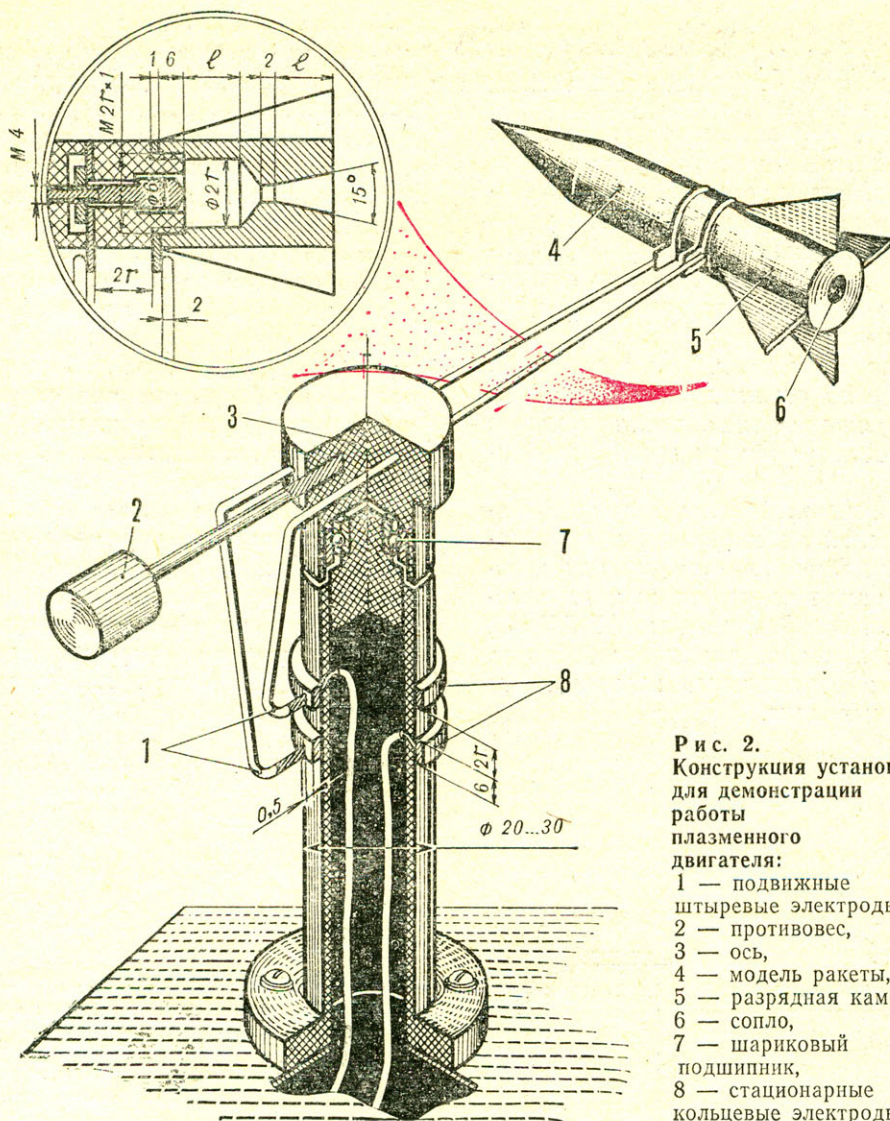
Конструкция установки для демонстрации работы плазменного двигателя:
